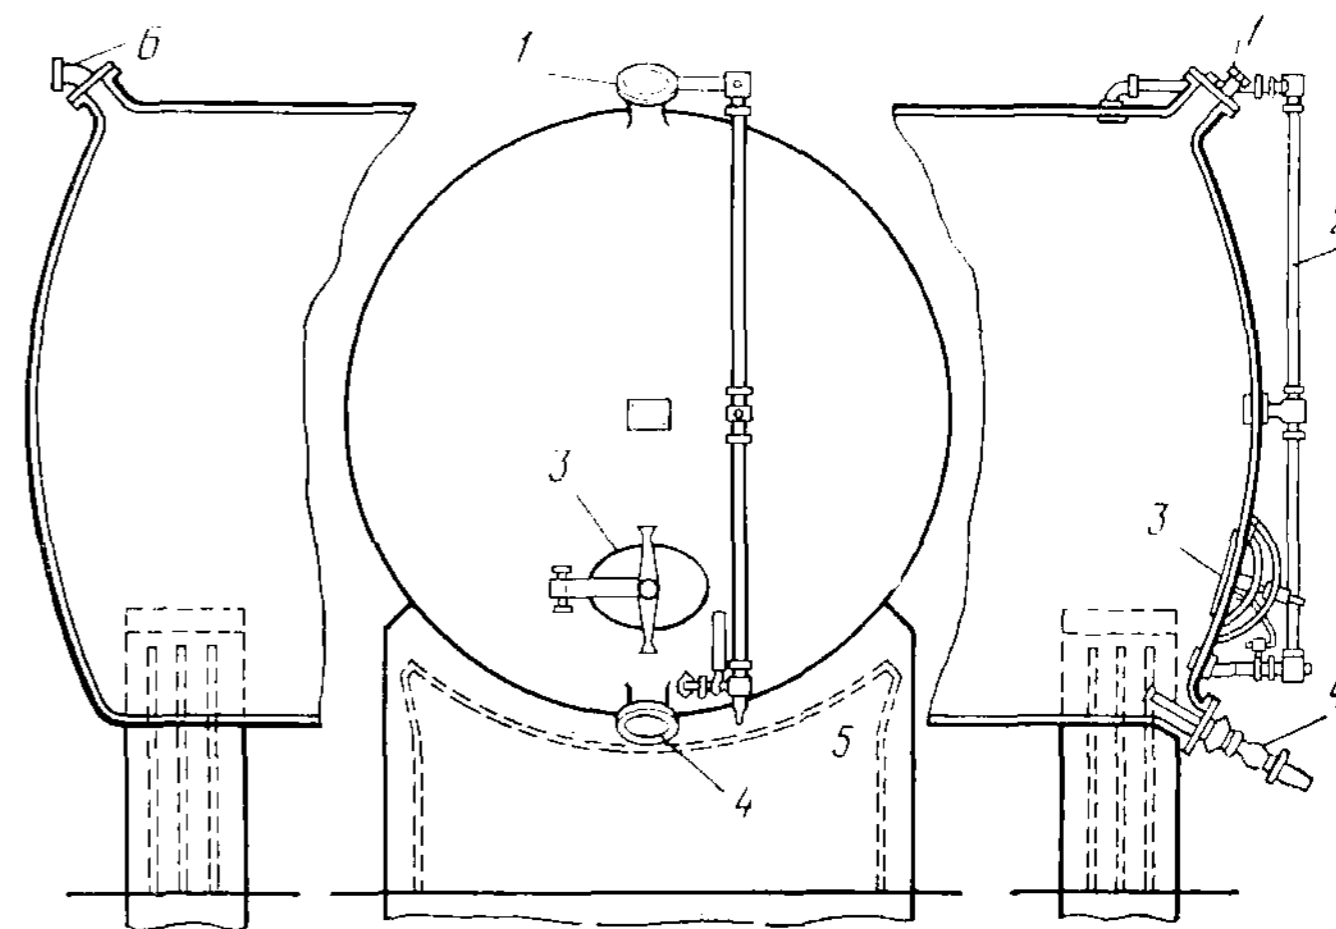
Цилиндрический горизонтальный металлический резервуар:
